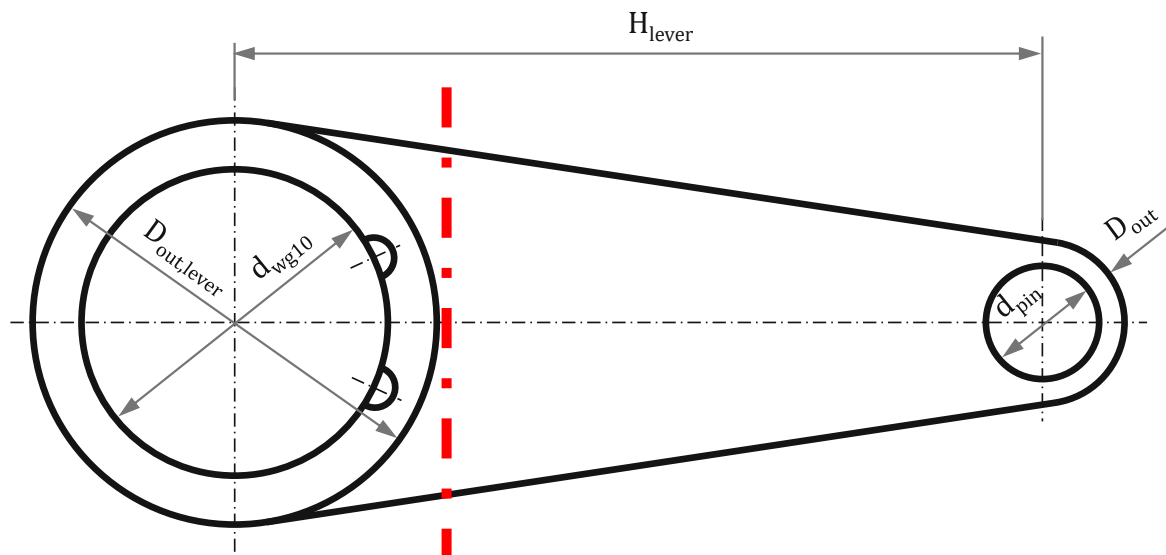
Skizze des Hebels für die Bauform mit Biegeleiker
